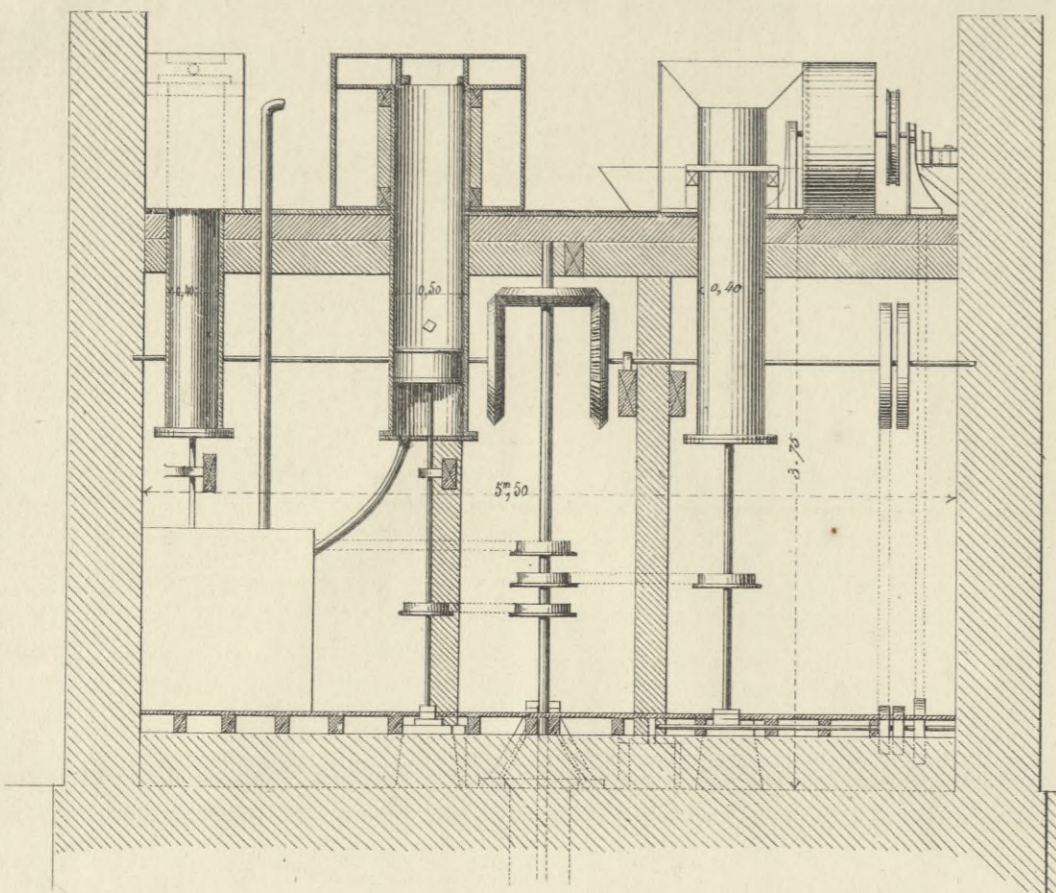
Plan à 0^m,02 pour 1^m00.
